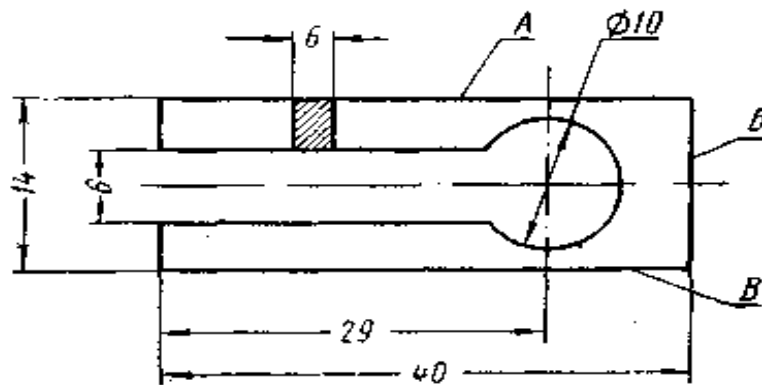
Ескіз зразка «вилочки» для випробувань на корозію під напругою
